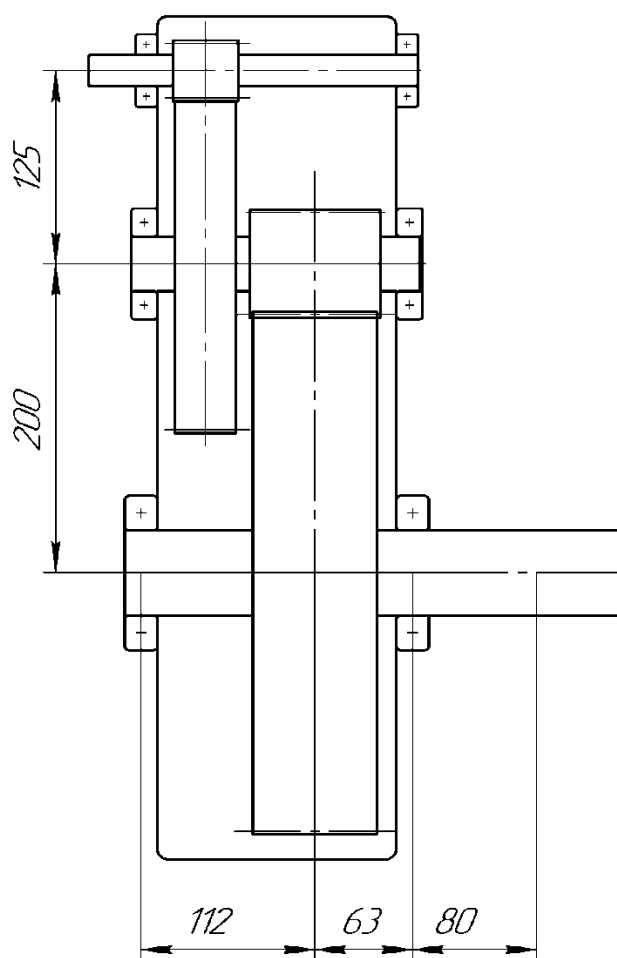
Компоновка циліндричного двохступінчастого редуктора
